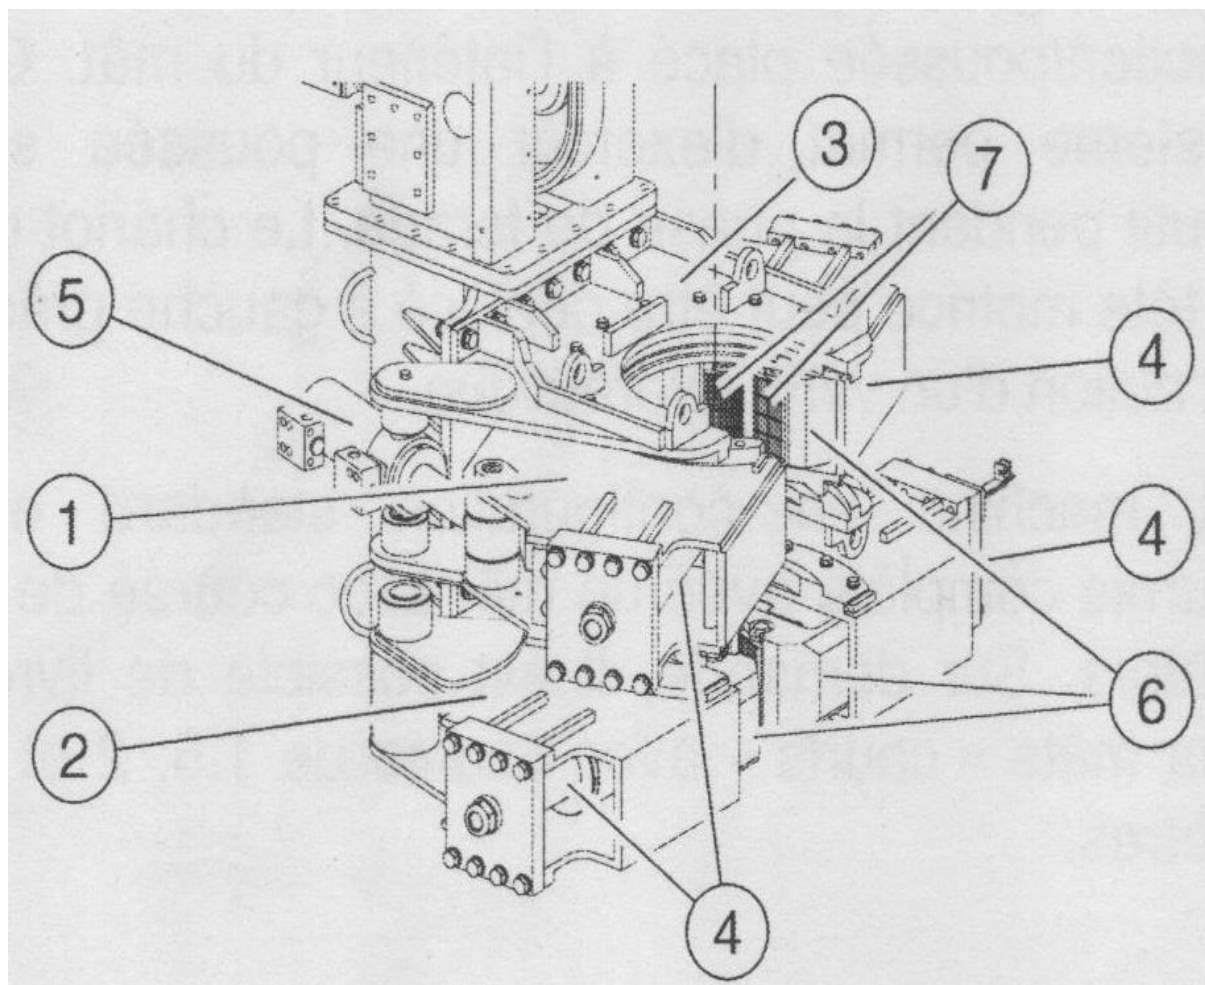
Mors de serrage /Mors de desserrage et guide tige
